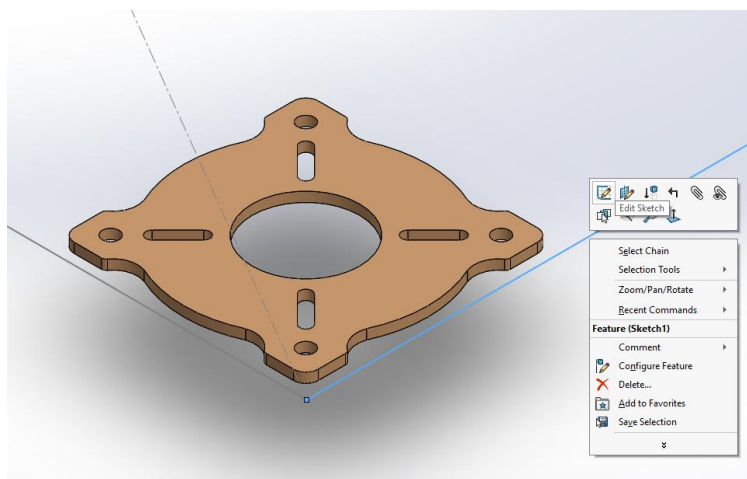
Povezivanje plavo označene površine dijela i „Top Plane“-a
